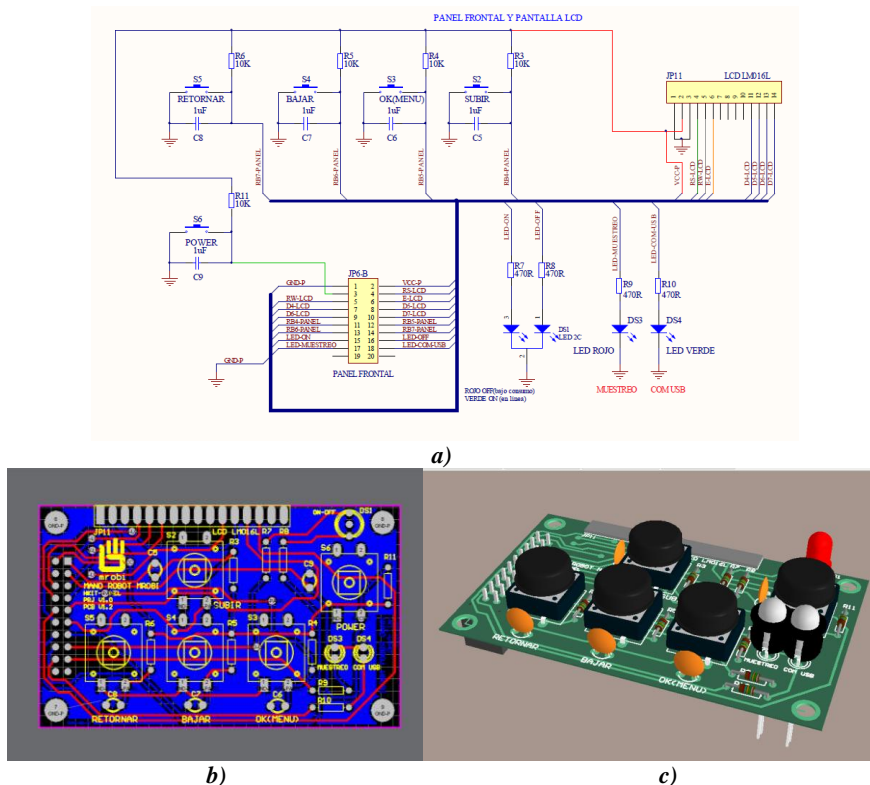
a) Esquema Electrónico del panel frontal. b) Vista frontal del la tarjeta. c) Vista 3D.
